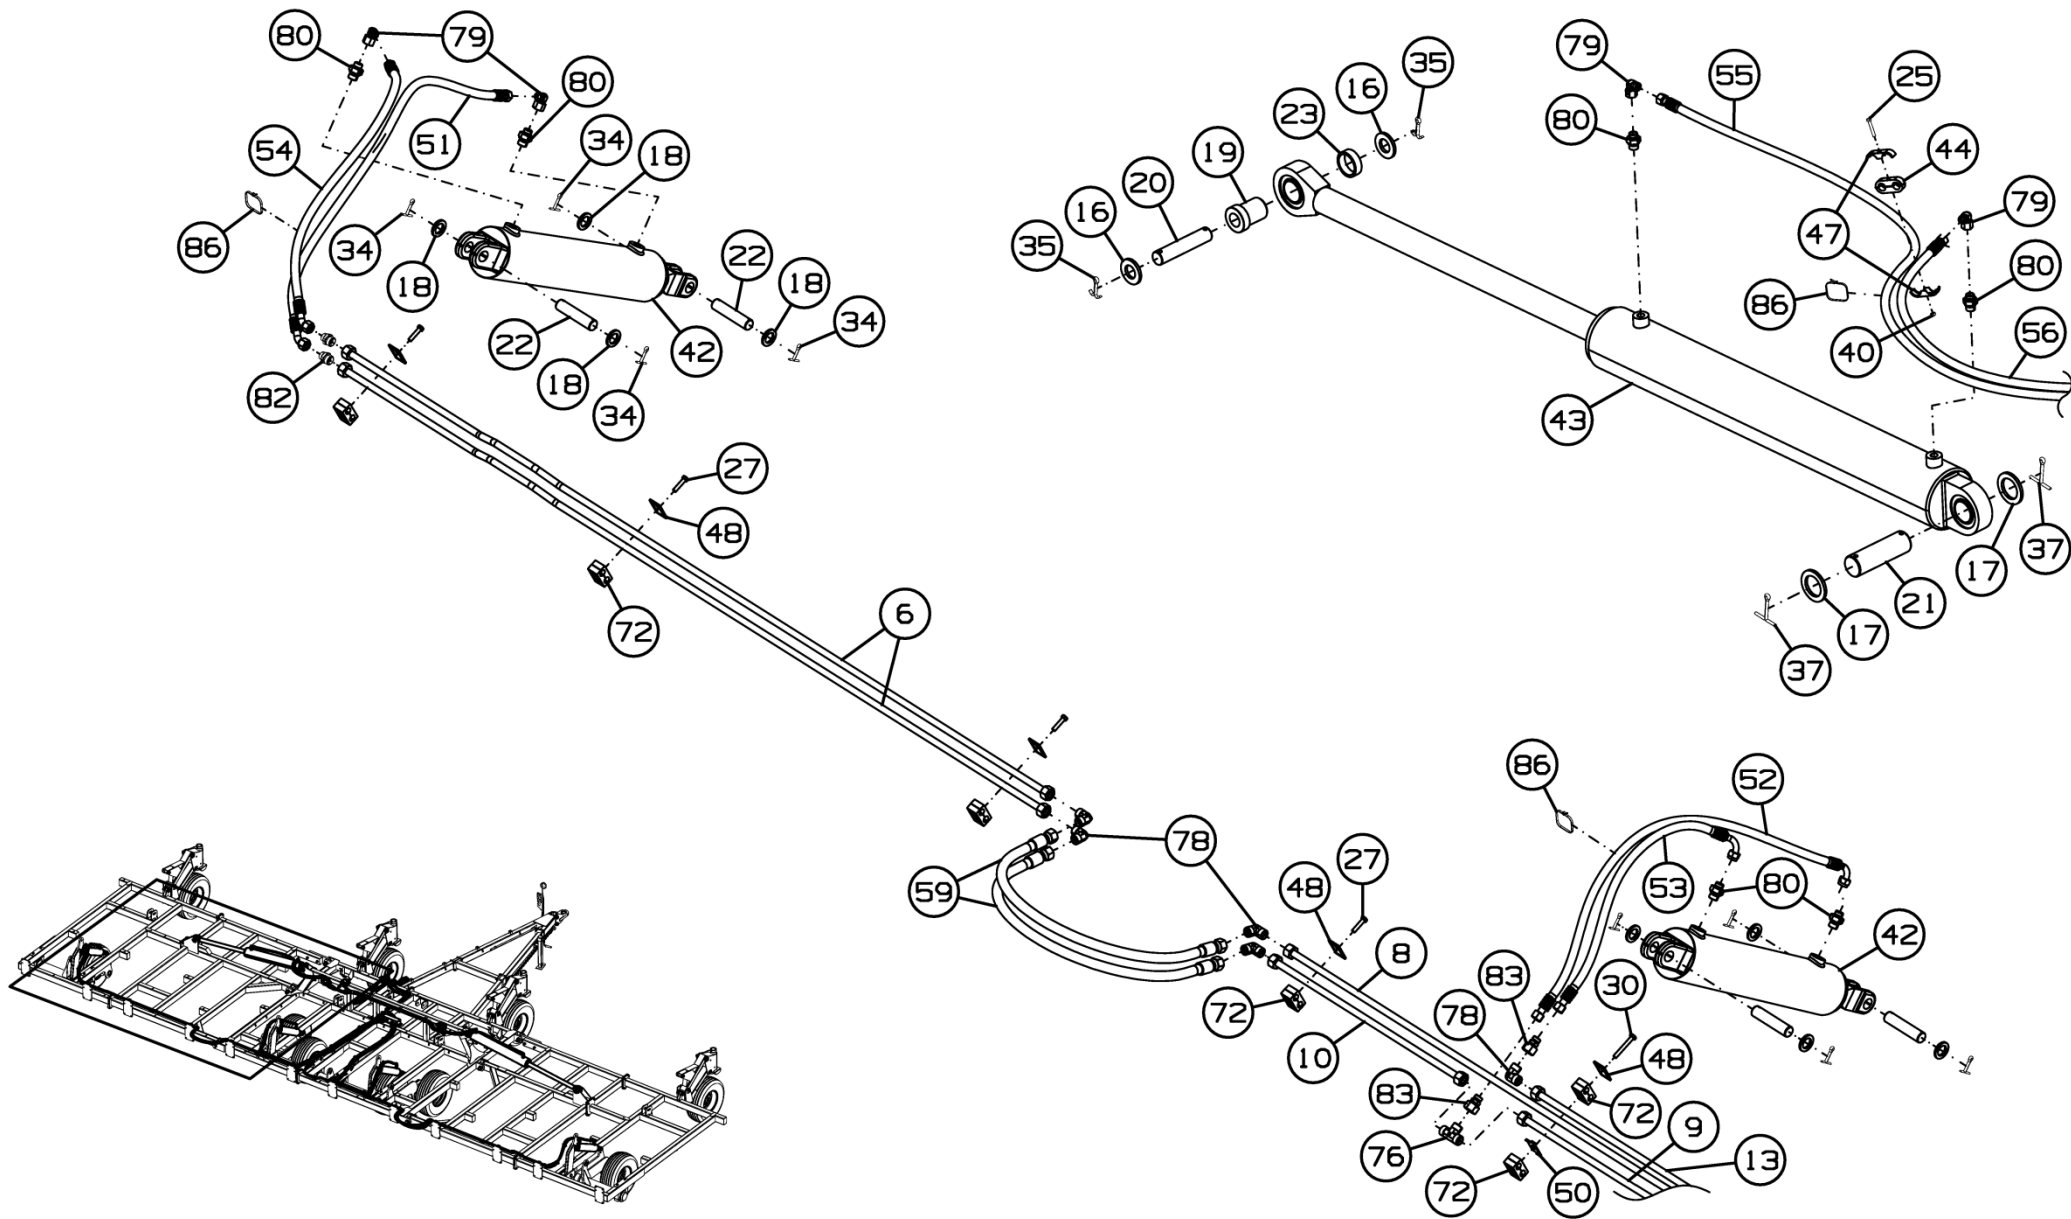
Установка гидрооборудования СГ-122.12.500
